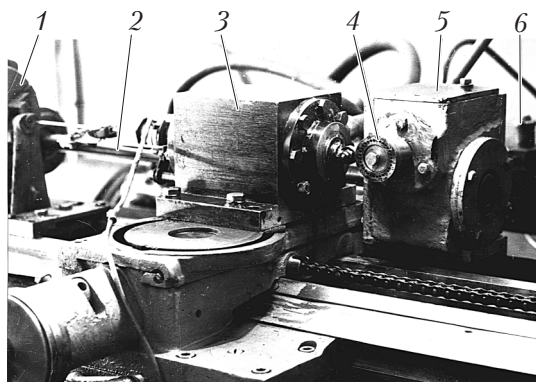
Виброустановка ВУ-1 на базе модернизированного токарного станка КТС-250:
